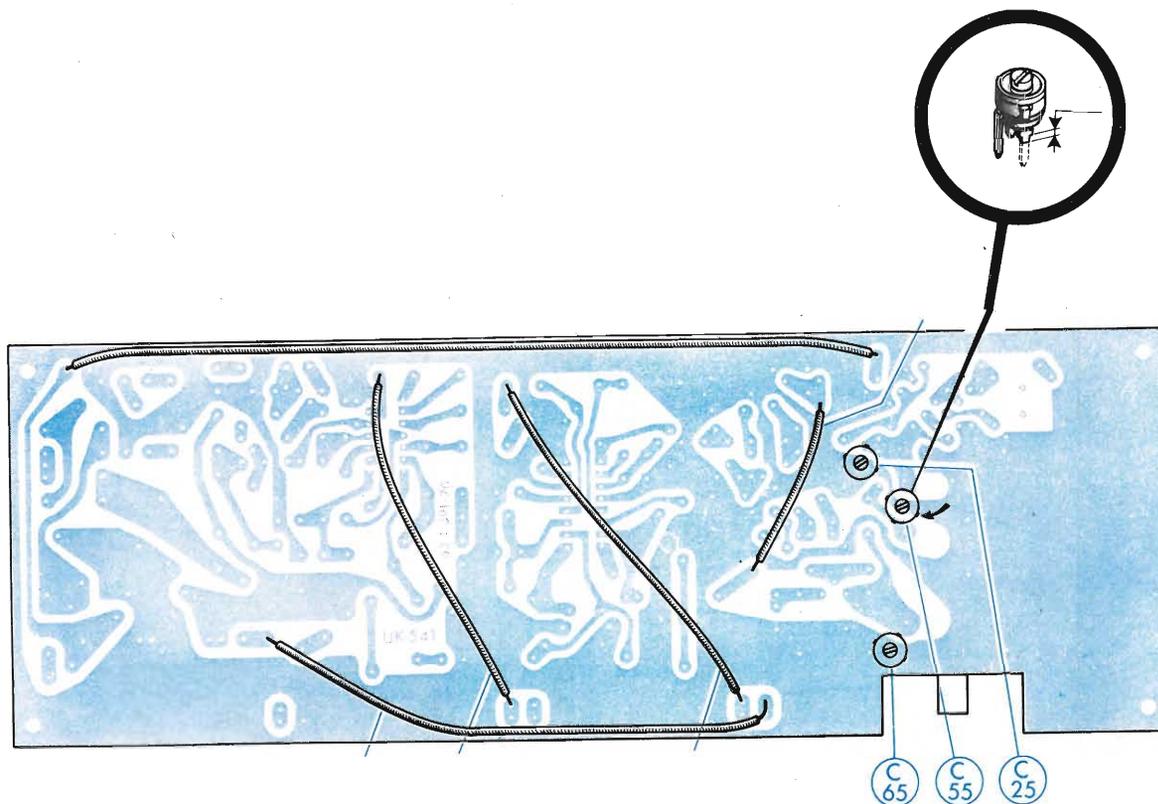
Collegamenti sul lato rame del circuito stampato.
